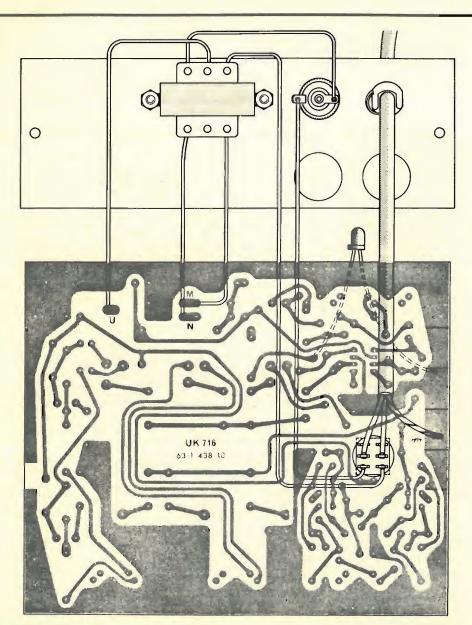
Cablaggio generale con le connessioni dettagliate impianto.
